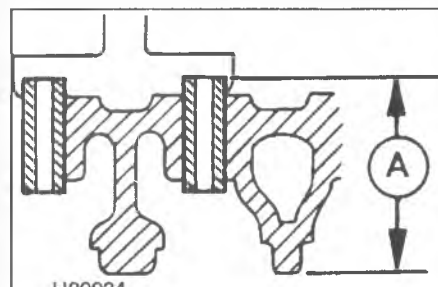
б. Измерение установочной высоты направляющей втулки клапана (А) – дизельный двигатель серии "L"
